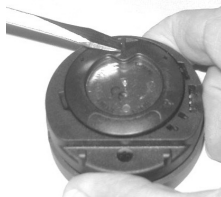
BAGUE DE FIXATION DU COUVERCLE
